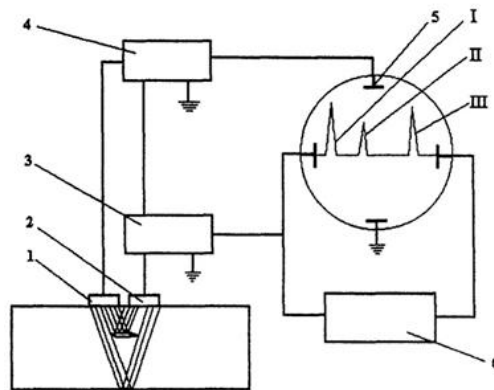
Схема ультразвукового контролю зварного шва
